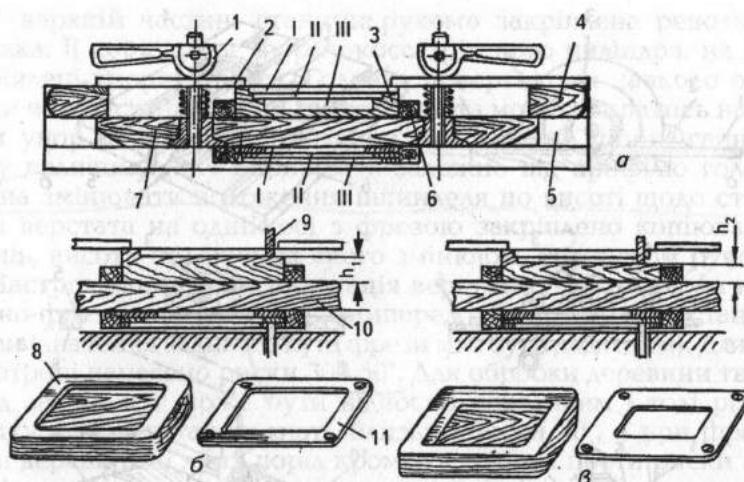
Фрезерування і послідовність обробки заготовок по шаблонам:
